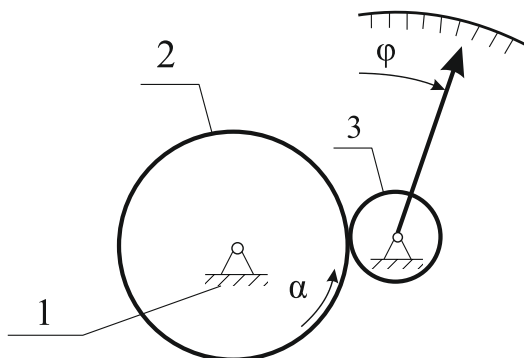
Зубчатая передача прибора: 1 - корпус; 2 - ведущее колесо; 3 - ведомое колесо
